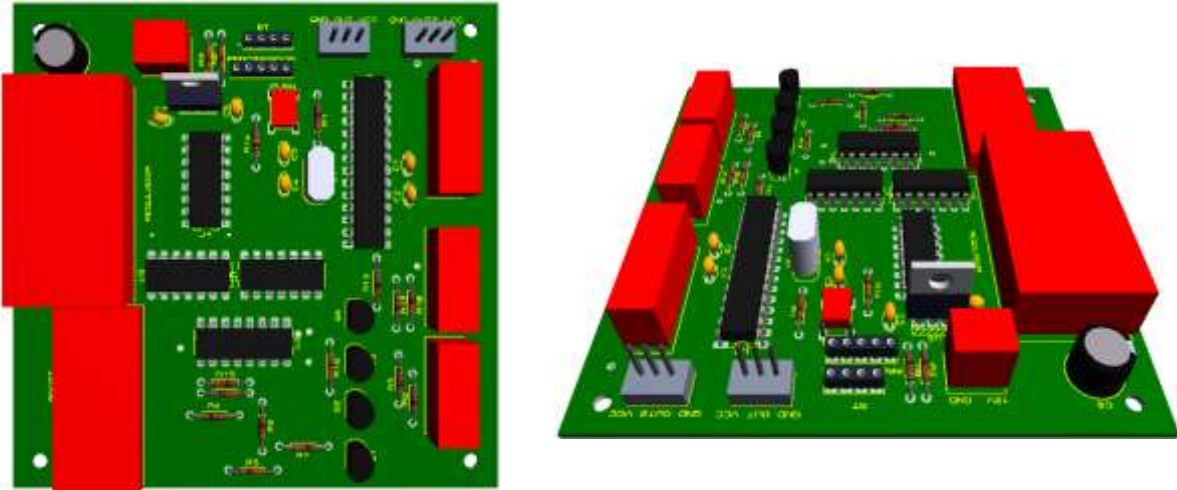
Diseño final de la tarjeta de control para la SRM.
